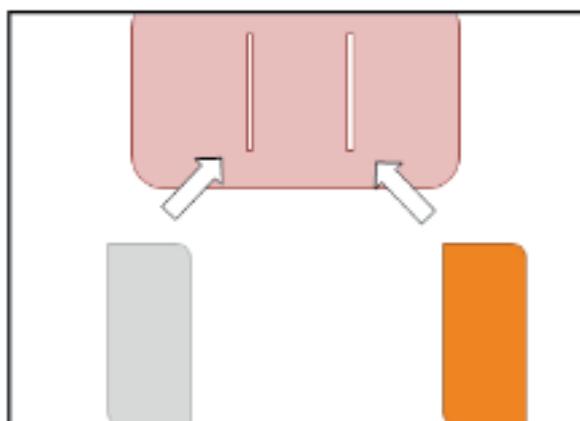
Encaixando as Placas Metálicas na Tampa do Pote.
